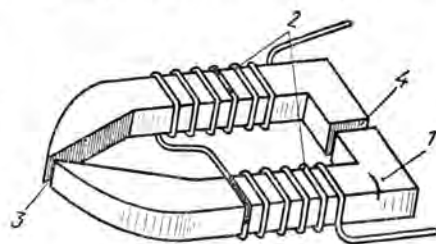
Устройство магнитной головки. 1 — сердечник; 2 — обмотка; 3 — передний (рабочий) зазор; 4 — задний (дополнительный) зазор.
